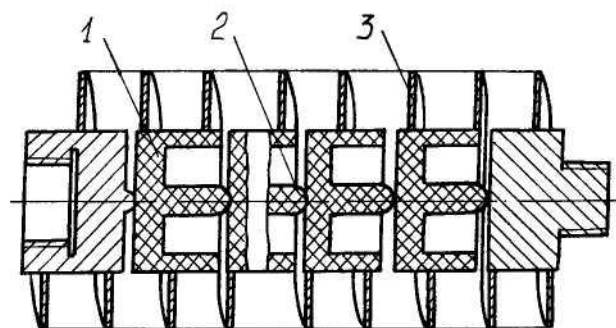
Робочі органи МГА з пластмасовими гнучкими валами
